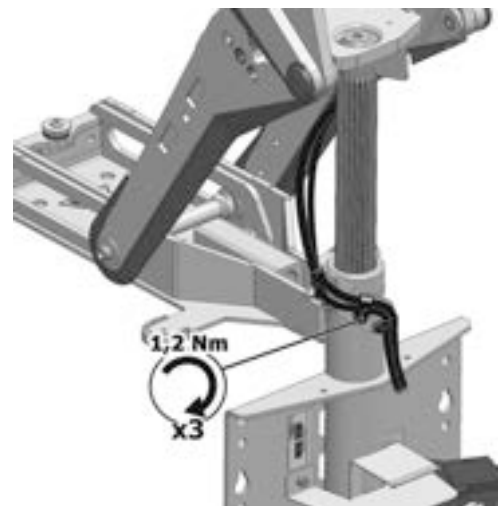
Das Kabel ist mit drei Kabelhalterungen an der Säule befestigt, die jeweils mit einer Schraube montiert sind.
